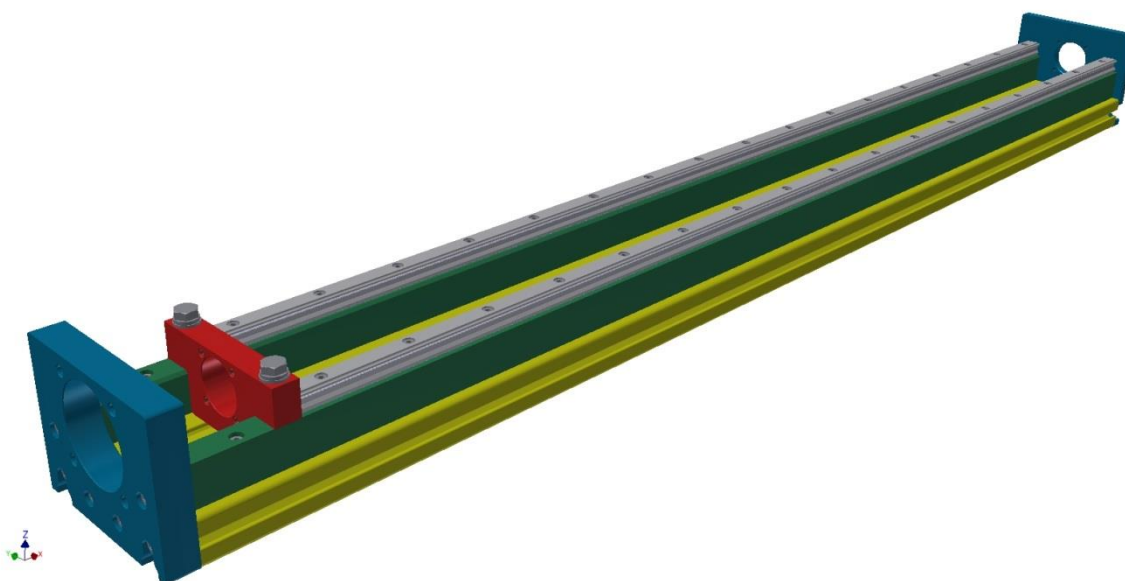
a) příruba pro uložení motoru b) příruba pro radiální ložisko
